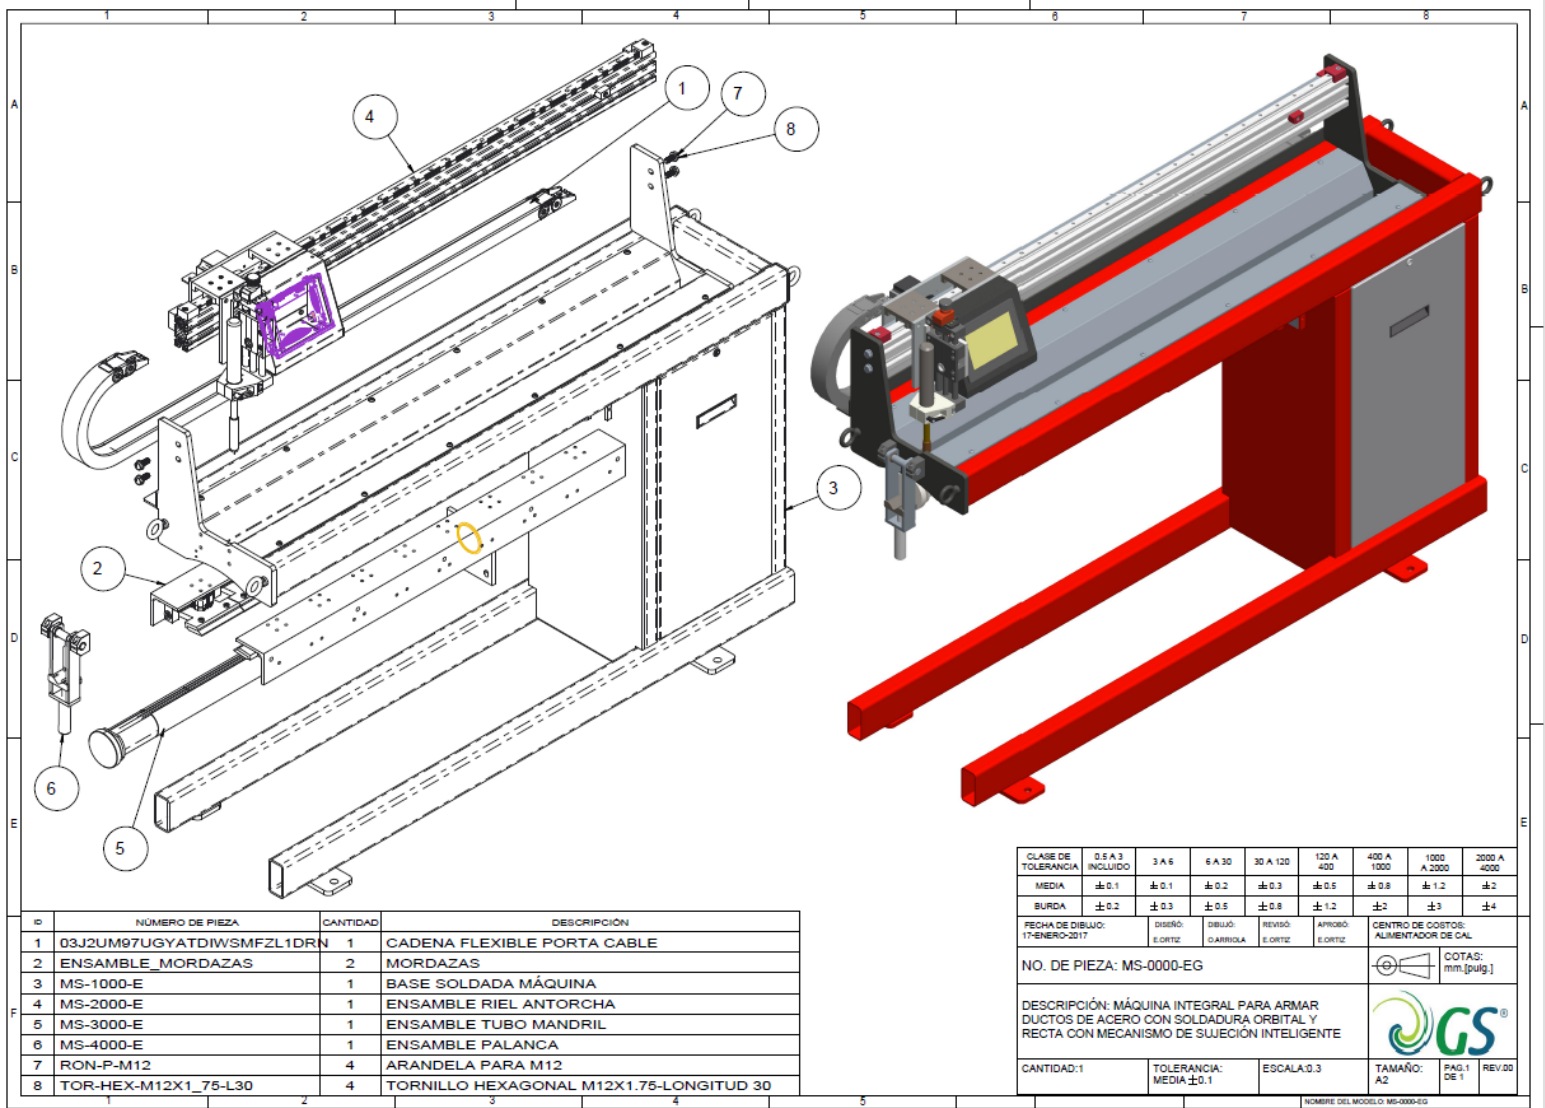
Plano de vista final de ensamble para la máquina de soldadura lineal y orbital para ductos de lámina (cortesía Green Spare)
